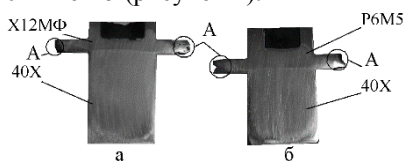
Вид биметаллических образцов полученных скоростным горячим выдавливанием: а) – рабочая часть образца (сталь X12MФ); основа образца (сталь 40X); б) – рабочая часть образца (сталь P6M5); основа образца
